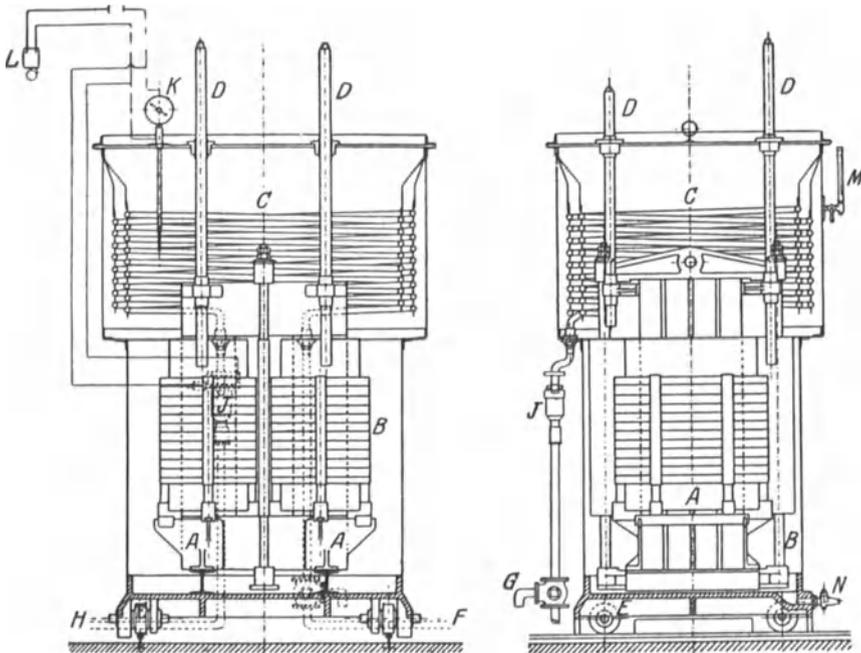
Schnitte durch einen Öltransformator (im Kessel) mit innerer Wasserkühlung (OWI). Kühlschlangen im Kessel eingebaut.
